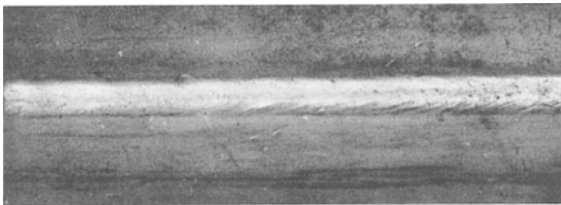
Aluminium-Kehlschweißnaht (2,5 mm-Blech).
